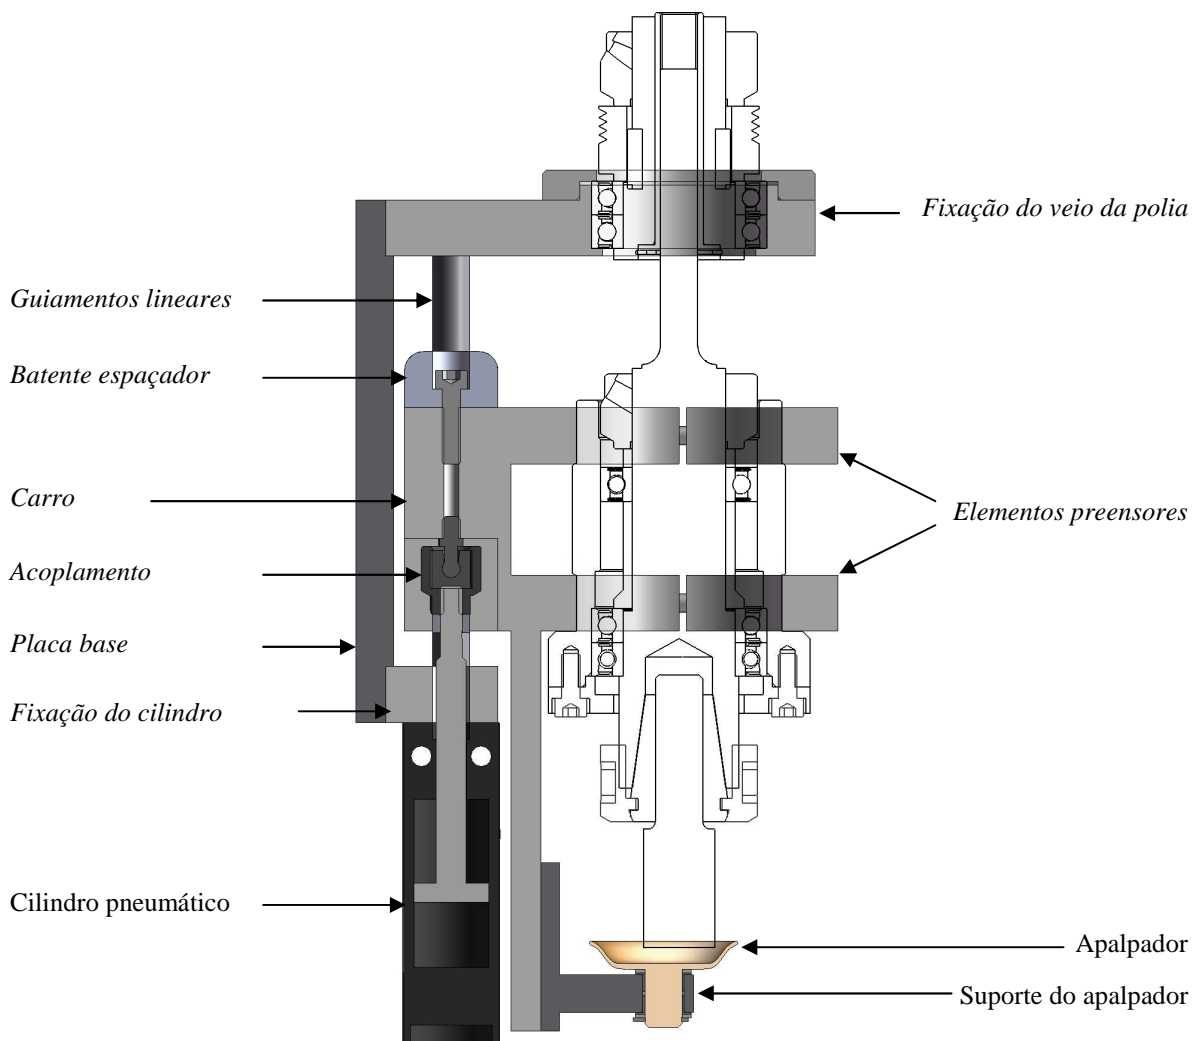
Vista em corte do sistema de suporte e elevação da árvore da ferramenta.
